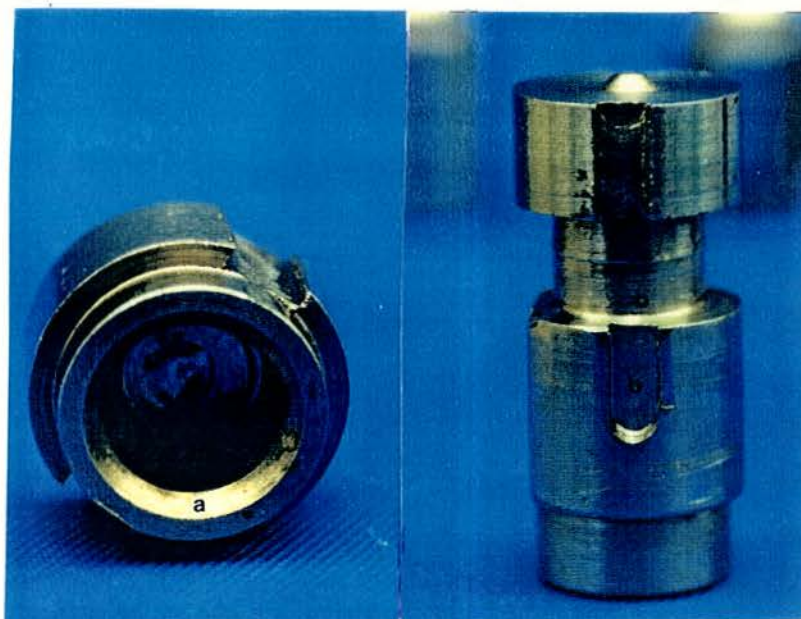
a) vista interna da cápsula metálica mostrando termino cervical em plano inclinado 135°; b) vista lateral do modelo-padrão com a cápsula metálica assentada. Notar o detalhe do sulco guia posicionado verticalmente na parede externa do modelo-padrão e da cápsula.
